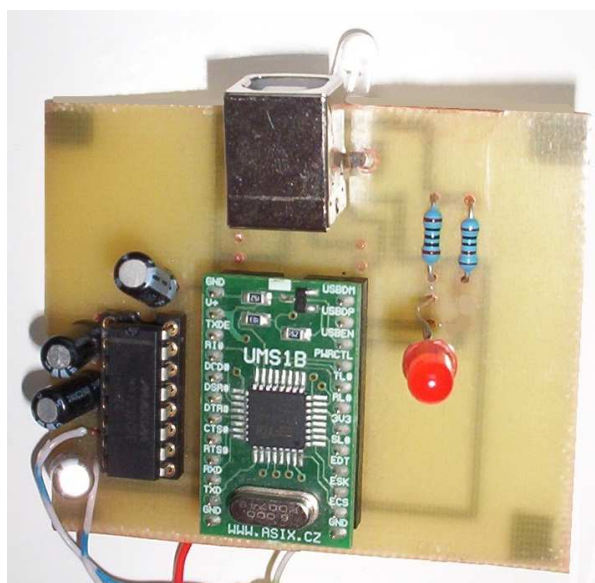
Deska plošných spojů pro operátorskou stanici
